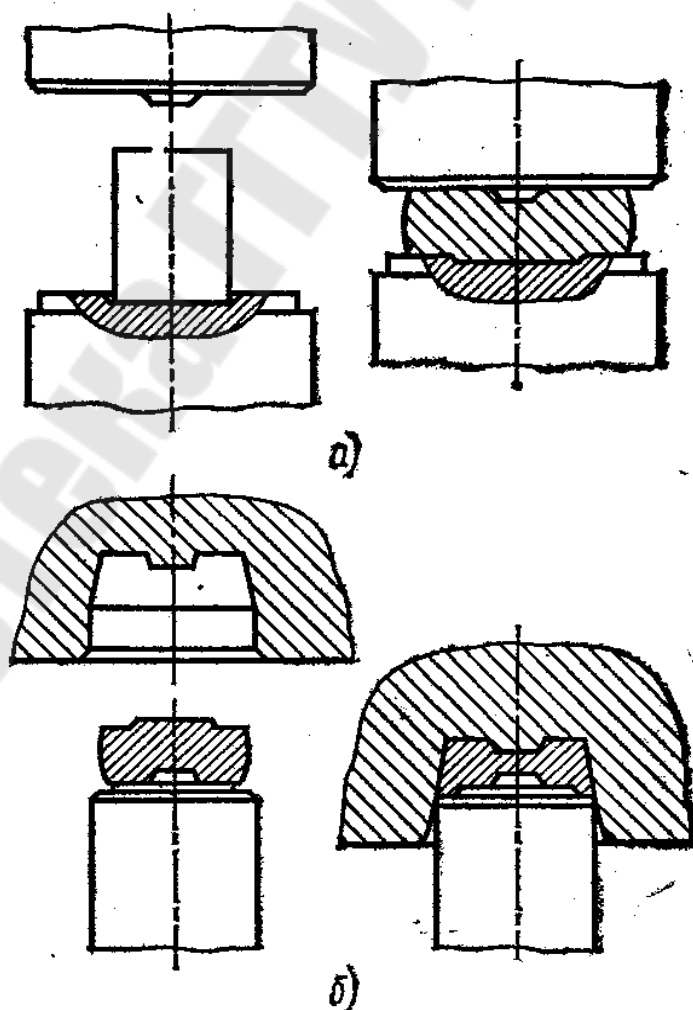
Штмп для безоблойной штамповки долбяков
